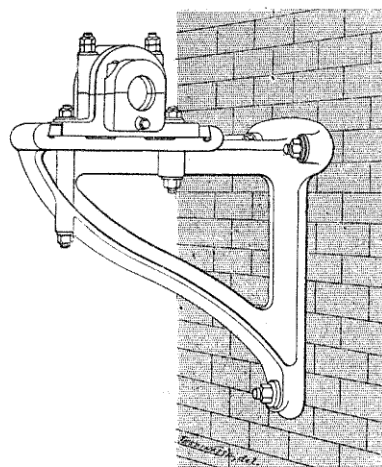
Chaise-console, type Piat, fixée à un mur.
